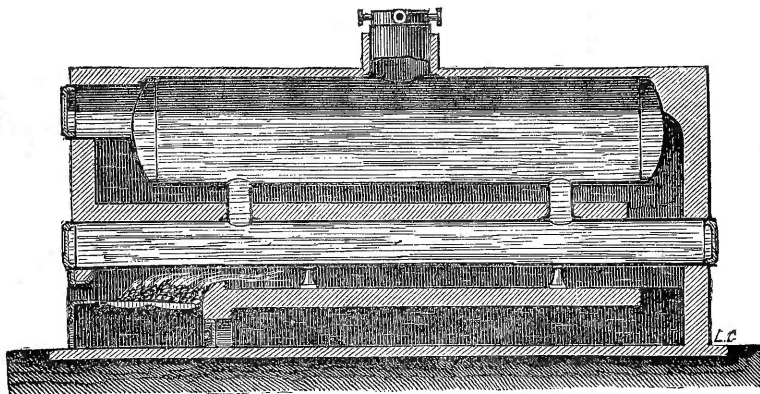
Coupe longitudinale d'une chaudière à bouilleurs.
